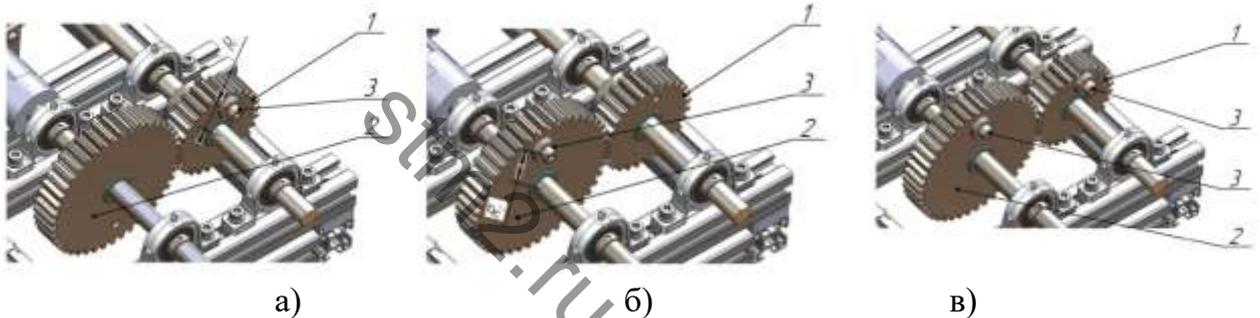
Схемы моделирования дисбаланса зубчатых колес: а) дисбаланс шестерни; б) дисбаланс колеса; в) дисбаланс шестерни и колеса
